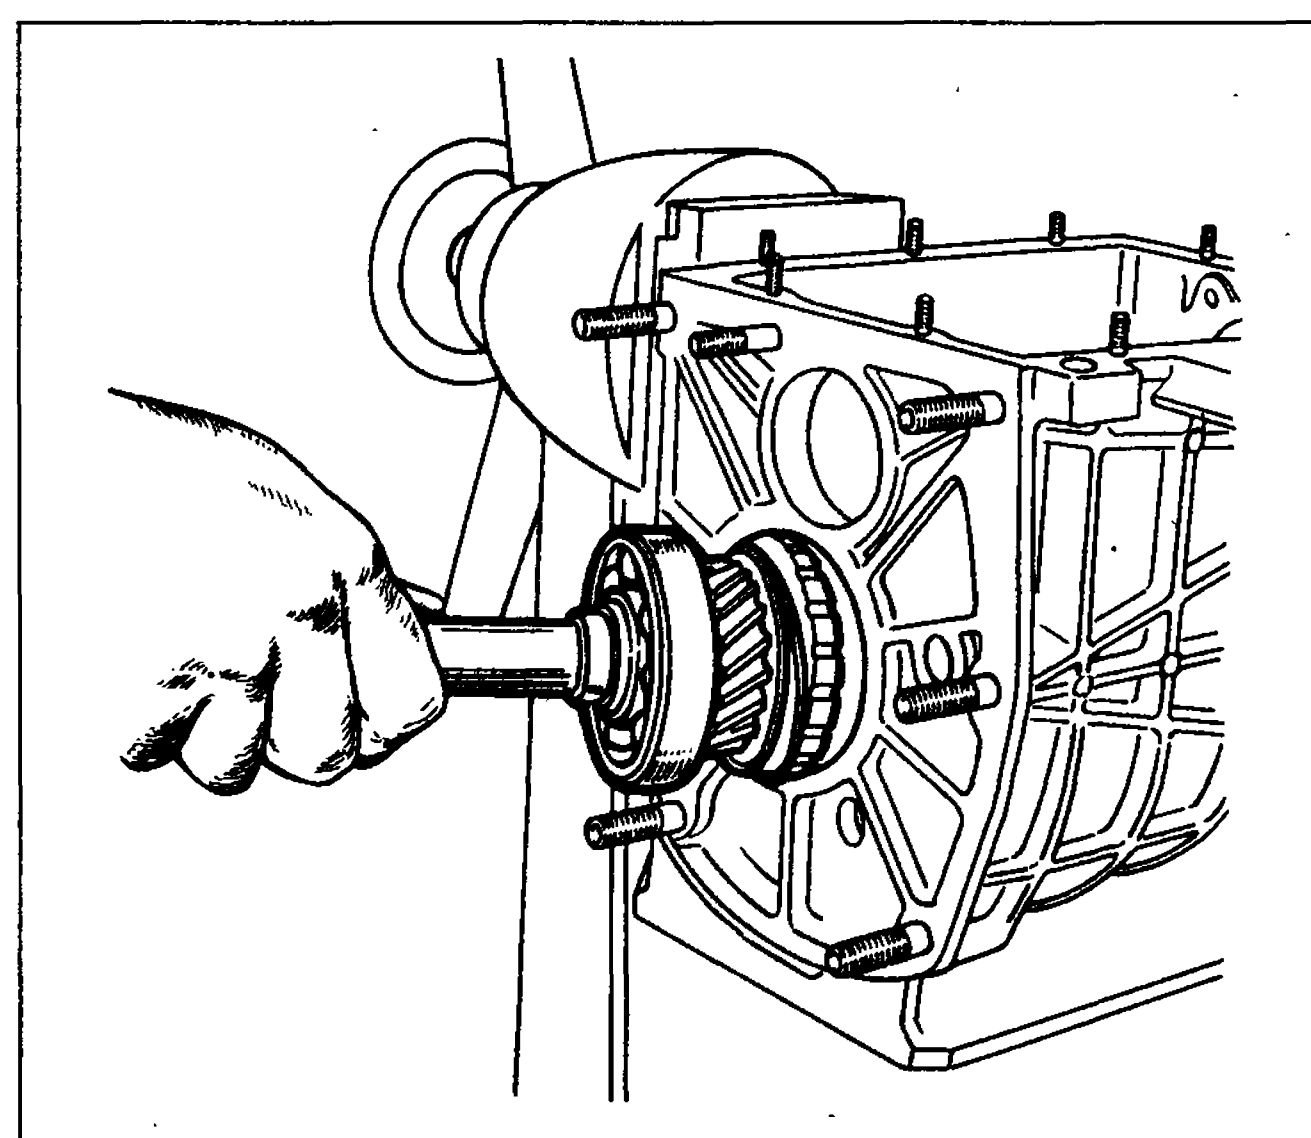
Извлечение промежуточного вала из картера коробки передач
